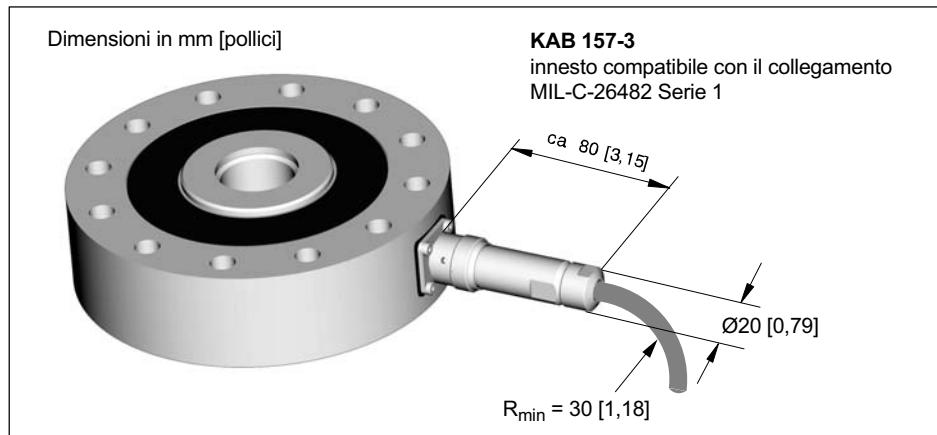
Ingombro d'installazione per spina di collegamento con attacco a baionetta
